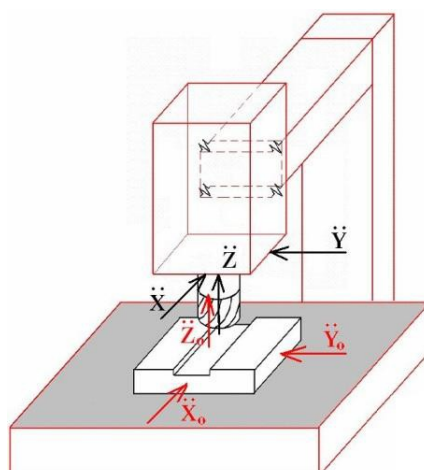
Модель шпинделя як твердого тіла із пружно-грузлими зв'язками з напрямними й станиною обробного центру DMC 635V
